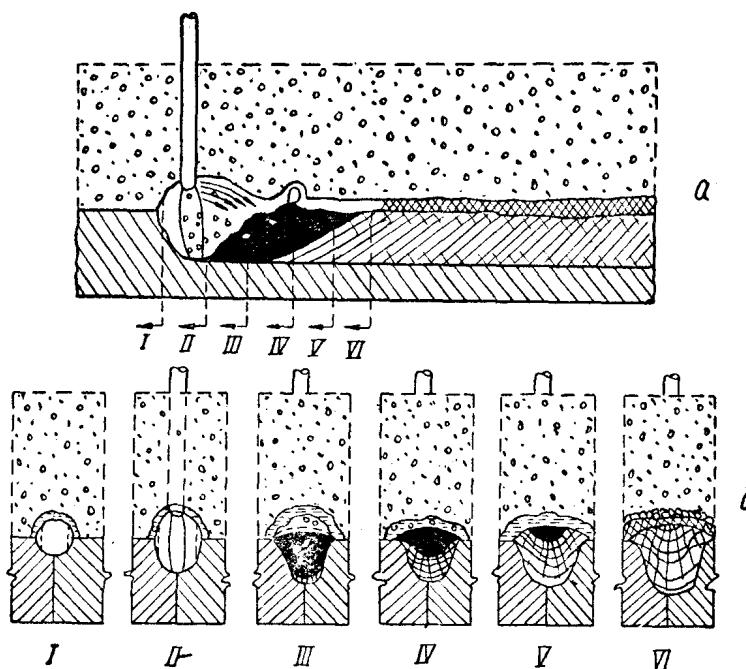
焊剂层下自动电弧焊的焊缝引成过程
